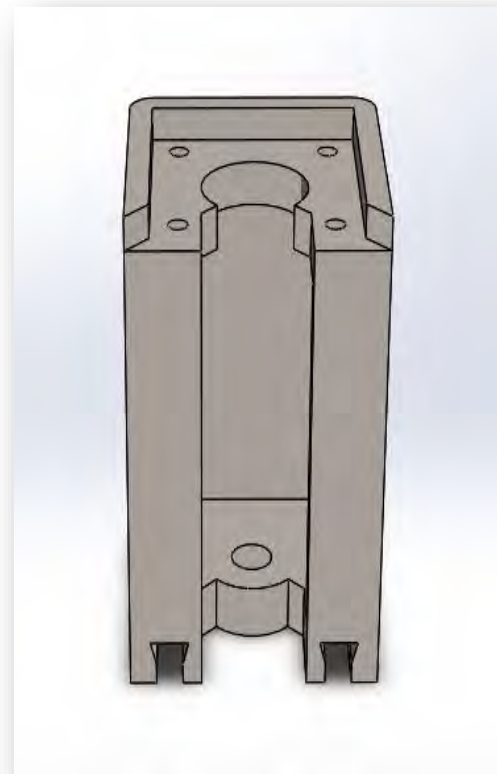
Ensamble husillo-embolo mediante el acoplamiento y base del actuador
